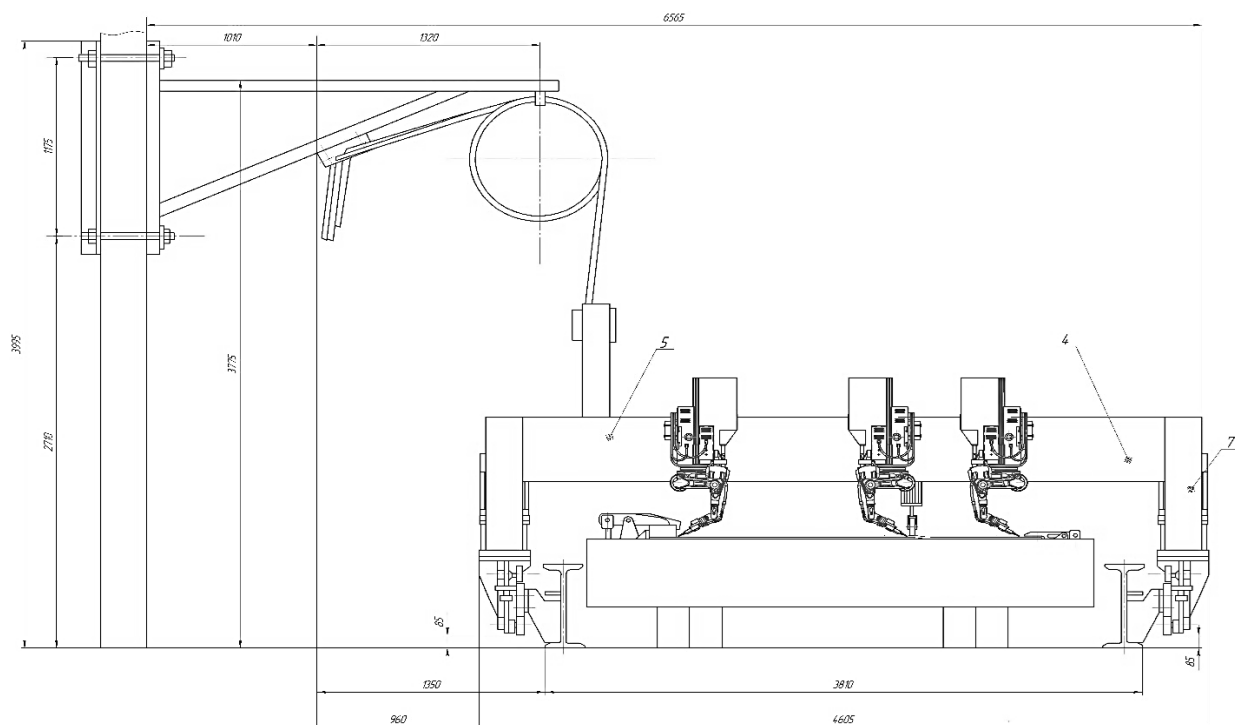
Портальна самохідна установка із трьома зварювальними головками
